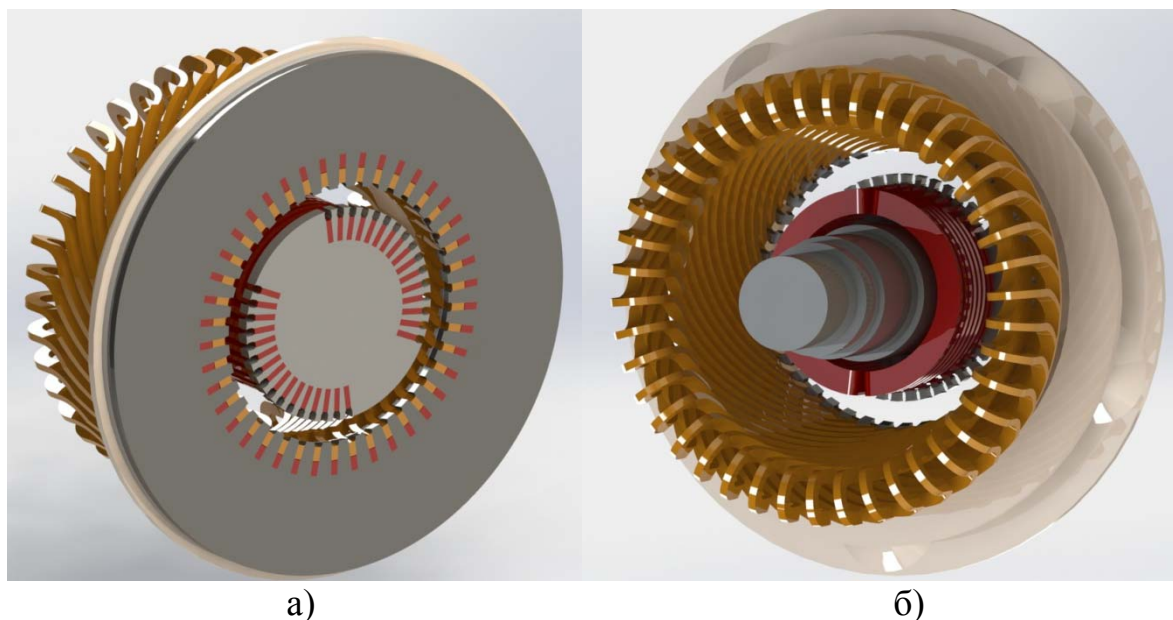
Конструкция торцевой зоны ТВВ-1000-2У3 (а – вид со стороны крайнего пакета; б – вид со стороны выступающего конца вала)
